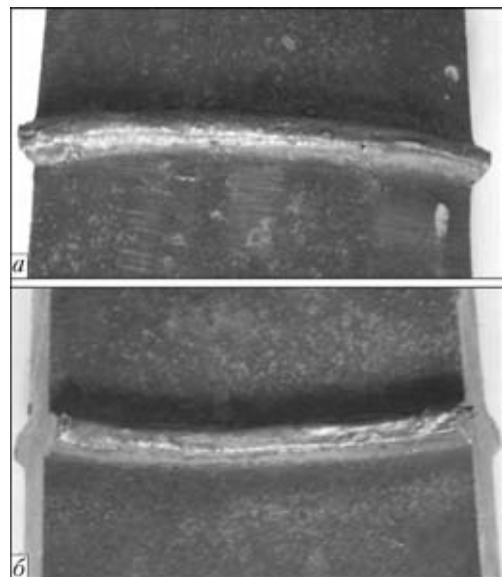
Формирование сварного соединения с внешней (а) и внутренней (б) сторон труб
